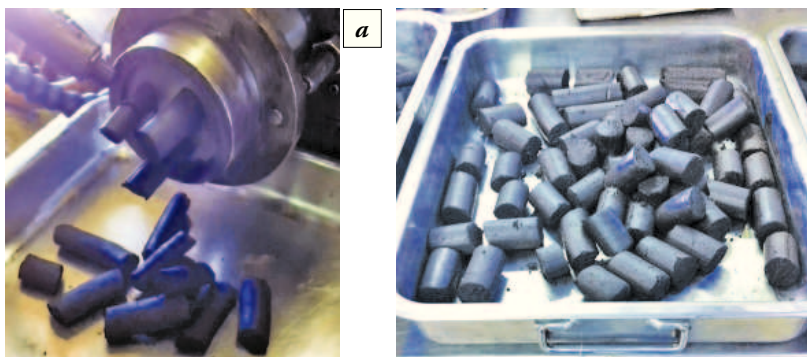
Образцы брэсков: а – изготовление брэсков; б – внешний вид рудоугольных брэсков
